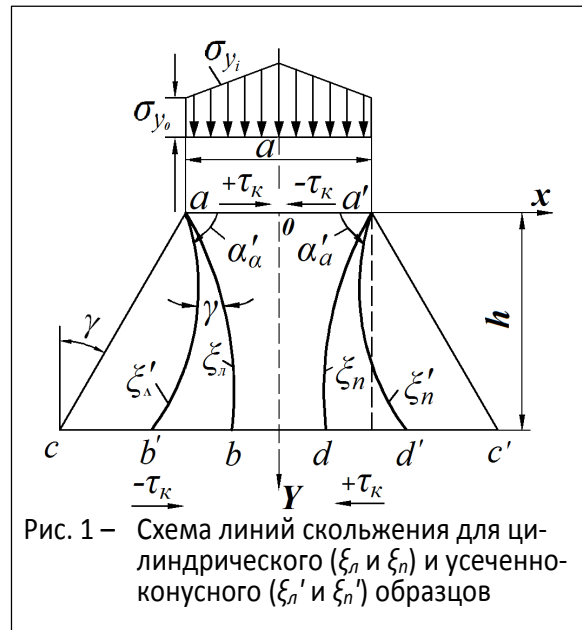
Схема линий скольжения для цилиндрического (ξ_l и ξ_n) и усеченно-конусного (ξ'_l и ξ'_n) образцов
